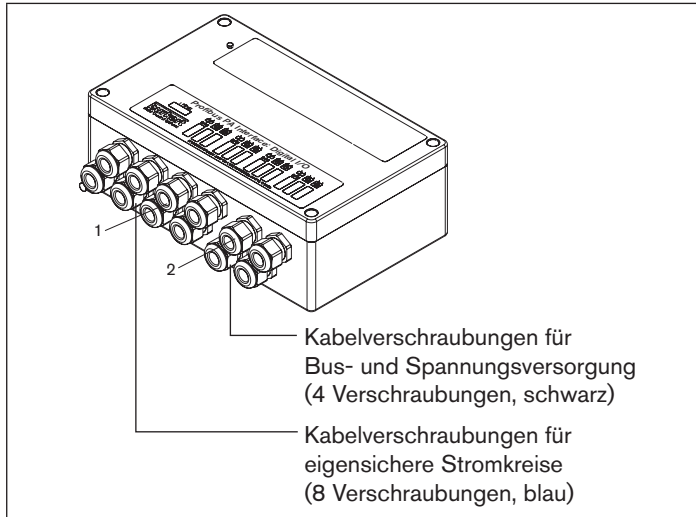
Lage der Kabelanschlüsse am Aluminiumgehäuse des Geräts
